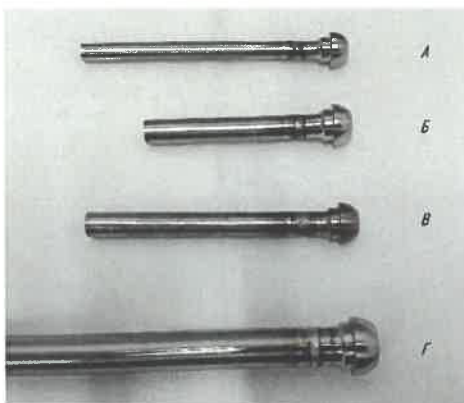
Трубчатые образцы после орбитальной сварки
